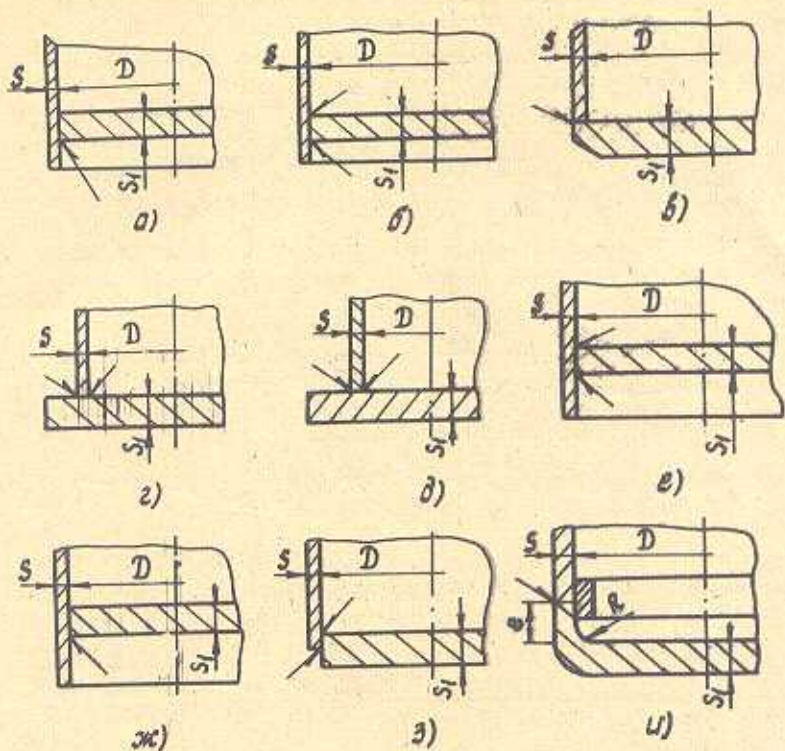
Конструкции плоских днищ и схемы соединения их с цилиндрическими обечайками: а – с односторонним угловым швом без скоса кромки; б, г, з – с двусторонним угловым швом без скоса кромки; в – с односторонним угловым швом и скосом двух кромок; д – с двусторонним угловым швом и двусторонним скосом кромки обечайки; е – с двусторонним скосом кромки днища; ж – с односторонним тавровым швом и криволинейным скосом кромки днища; и – с односторонним стыковым швом и подкладной
